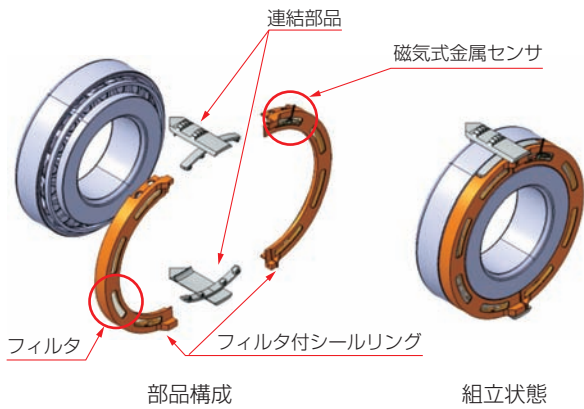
早期異常検知機能付円すいころ軸受 "Tapered Roller Bearings" with early failure detection sensor
